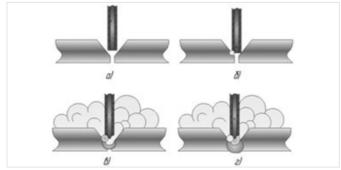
Схема процесса плавления порошковой проволоки при стыковке секций трубопроводов. а) подача порошковой проволоки в зону сварки стыка трубопровода; б) короткое замыкание и образование разряда; в) образование сварочной дуги, оплавление кромок свариваемых труб и образование защитного газа; г) образование капли расплавленного металла и
